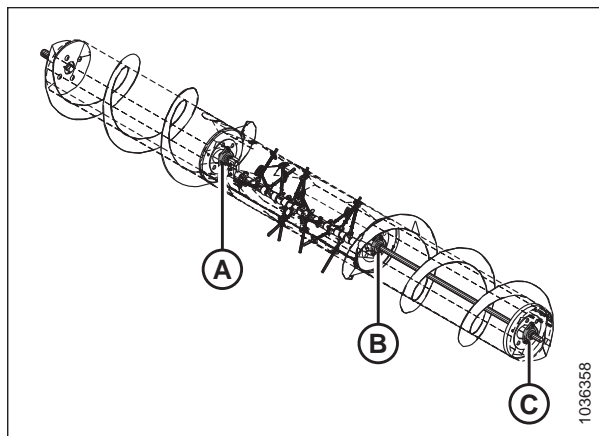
Подшипники с пресс-масленкой на шнеке — вид справа
